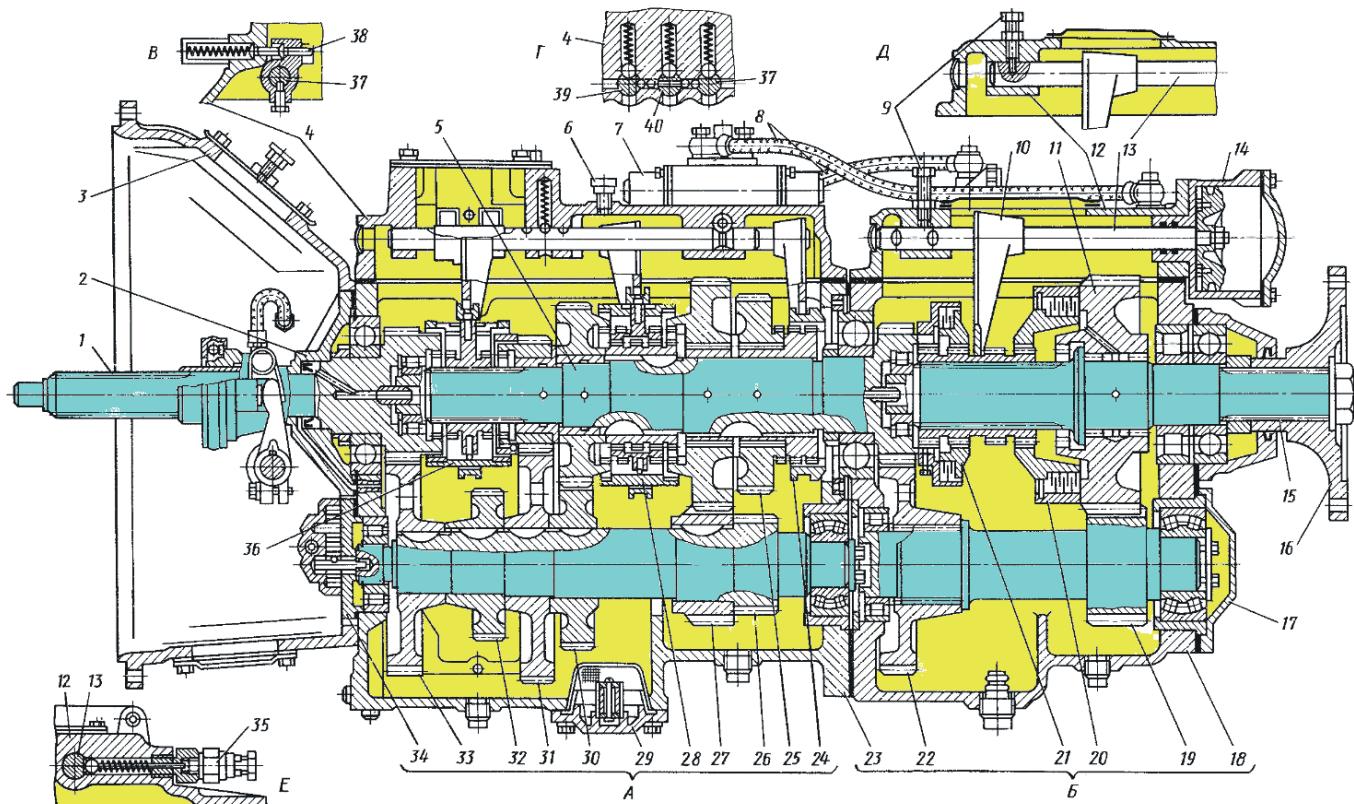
Коробка передач: А — основная коробка; Б — дополнительная коробка; В — предохранитель включения заднего хода; Г — разрез по фиксаторам и замкам штоков в основной коробке; Д — стопорное устройство для выключения дополнительной коробки при буксировке автомобиля; Е — датчик сигнализатора включения дополнительной коробки.
